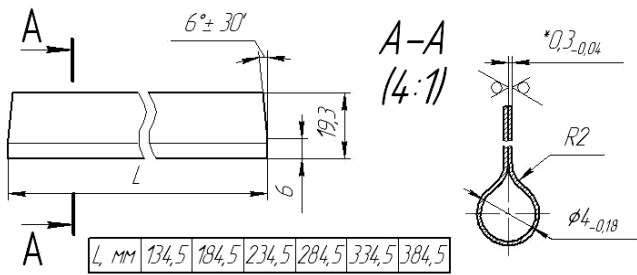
Чертеж детали «шторка» вентиляционной решетки
